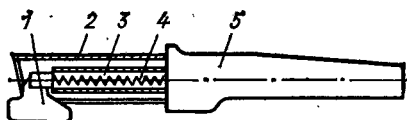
Прибор для сваривания полиэтиленовой пленки «Молния-2»
